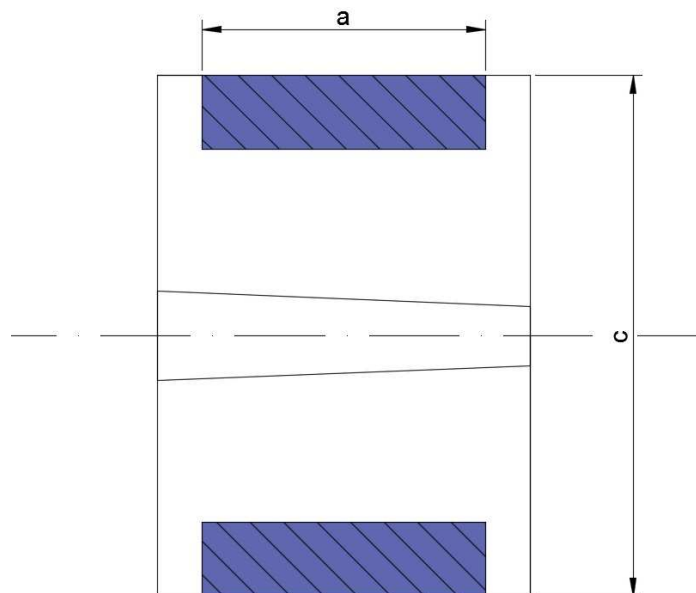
Řez vnějším rotorem s hlavními rozměry
